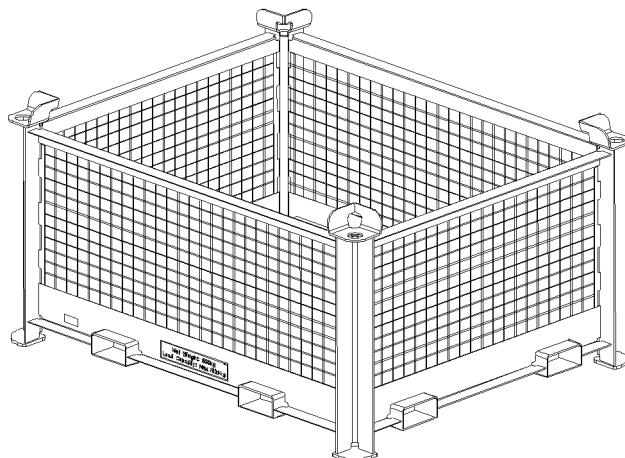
Caja de transporte para cables de anclaje de fibra
